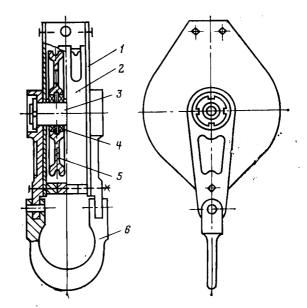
Талевый блок: 1 — щека; 2 — боковой кожух; 3 — ось шкивов; 4 — подшипник; 5 — шкив; 6 — серьга
